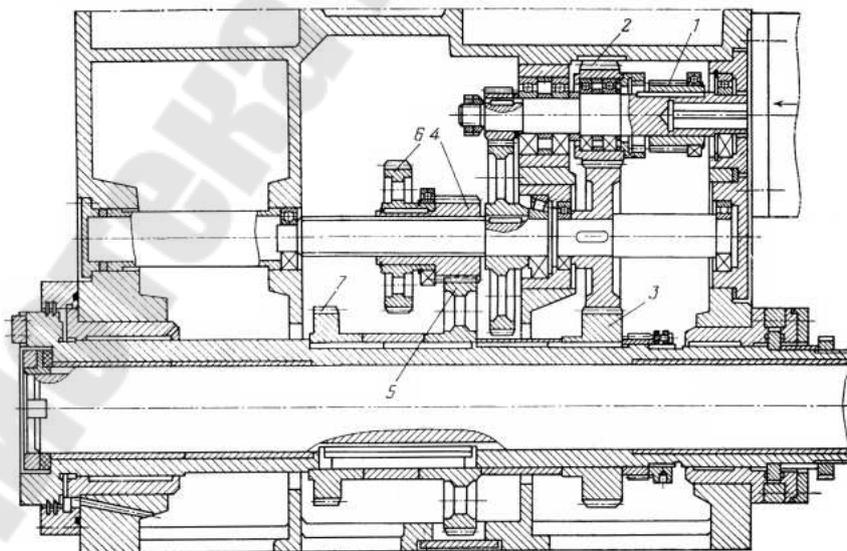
Шпиндельный узел горизонтально-расточного станка
